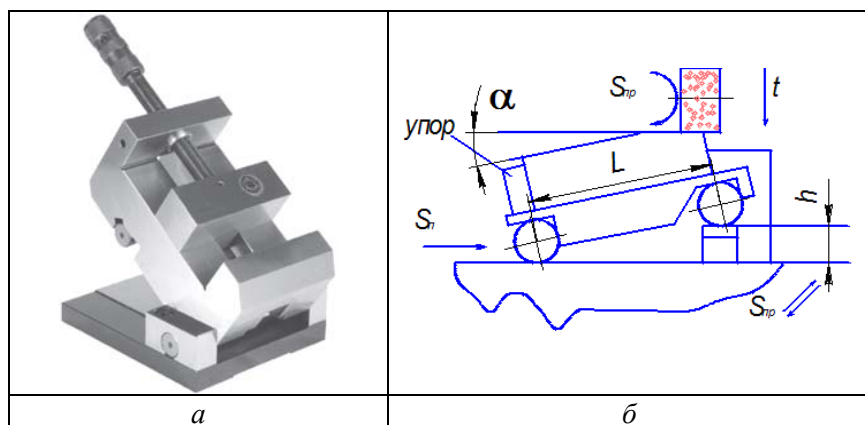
Синусное приспособление и схема его настройки для шлифования
